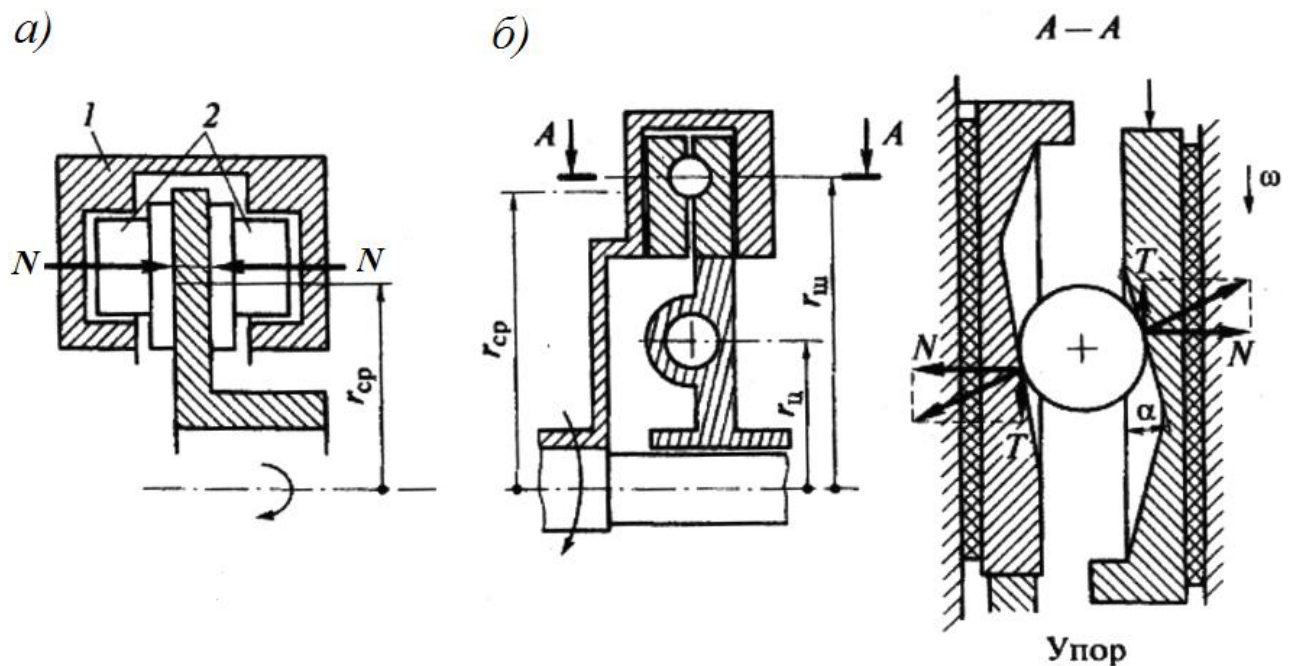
а, б* – Схеми дискових гальмівних механізмів: *а* - з обертовим диском; *б* - з обертовим корпусом: 1 - корпус; 2 - поршень
